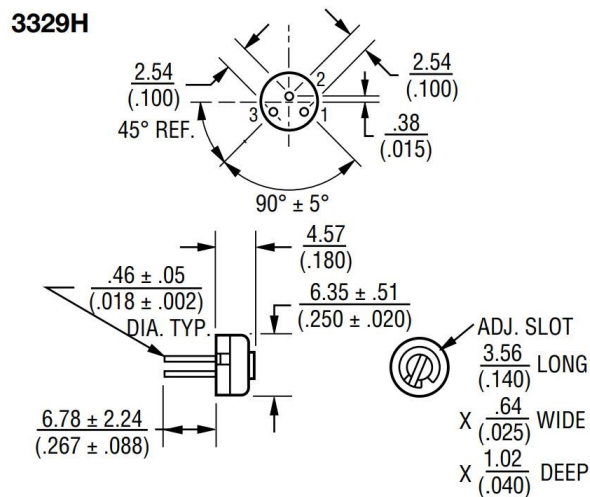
Габаритні розміри резистора 3329Н-1-3,3 кОм "Bourns"
